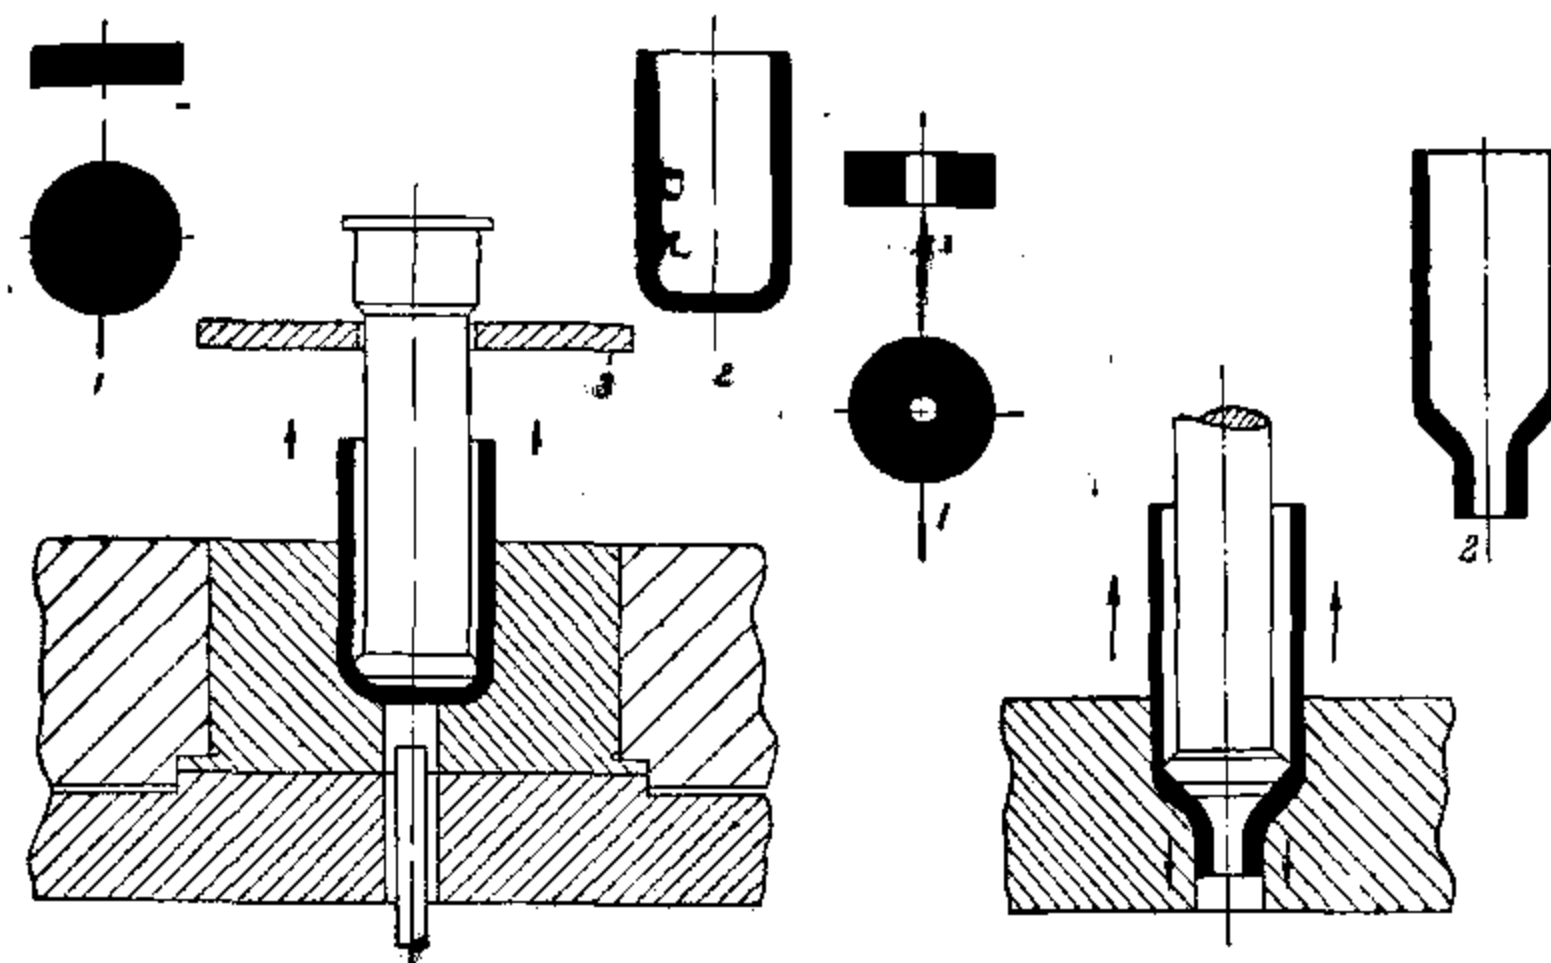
Обратный способ выдавливания из толстостенной заготовки 1 цилиндрического тонкостенного полого изделия 2; 3 — съемник
